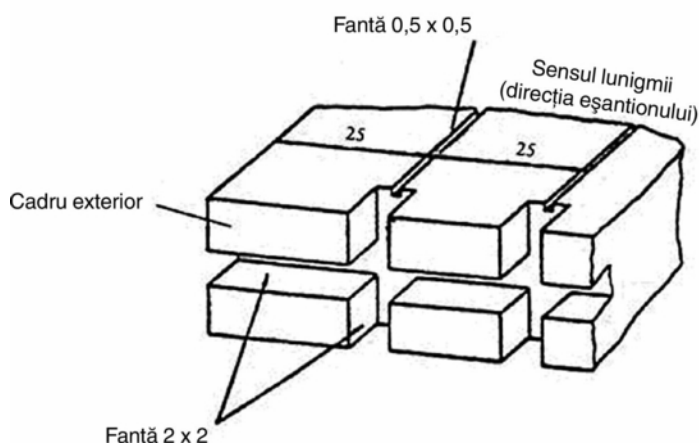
Exemplu de secțiune prin cadrul în formă de U al suportului metalic
